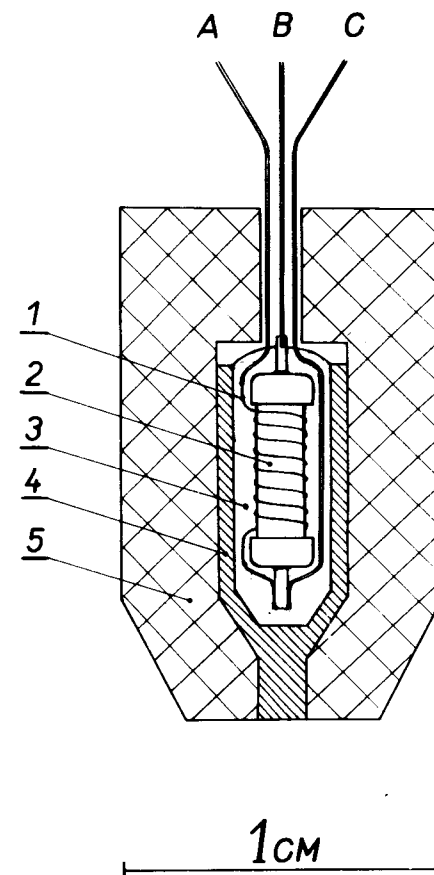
Конструкция датчика уровня жидкого гелия: 1 - изолированная сверхпроводящая проволока; 2 - резистор; 3 - эпоксидный клей; 4 - медный корпус; 5 - теплоизоляция.
